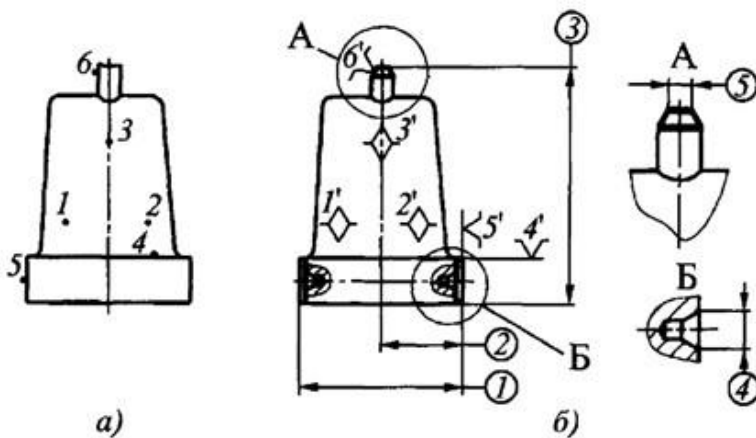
Схема створення нових технологічних баз для механічної обробки від баз заготовки: а – розташування баз заготовки; б – бази, сформовані під час механічної обробки.
